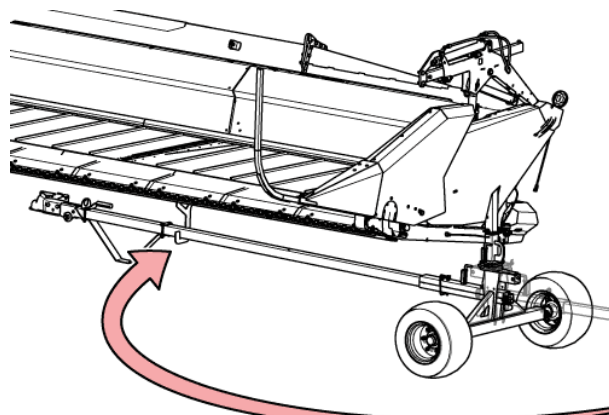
Поворот сцепного стержня в положение для хранения.
